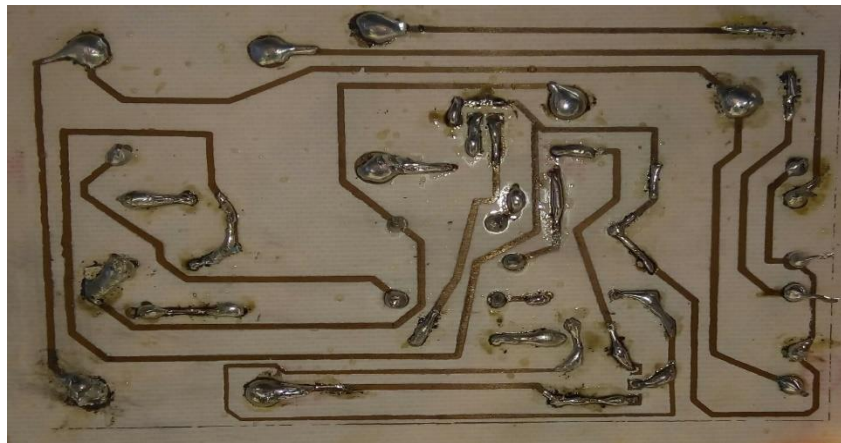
Ilustración de tarjeta electrónica regulador de carga soldada.
